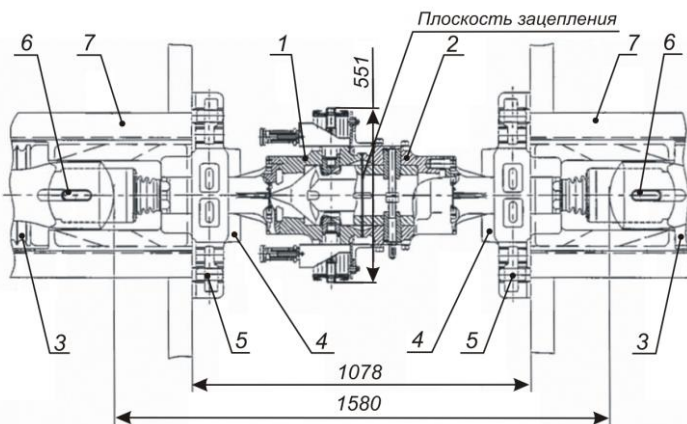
Схема безззорного сцепного устройства БСУ-3 (вид в плане):
